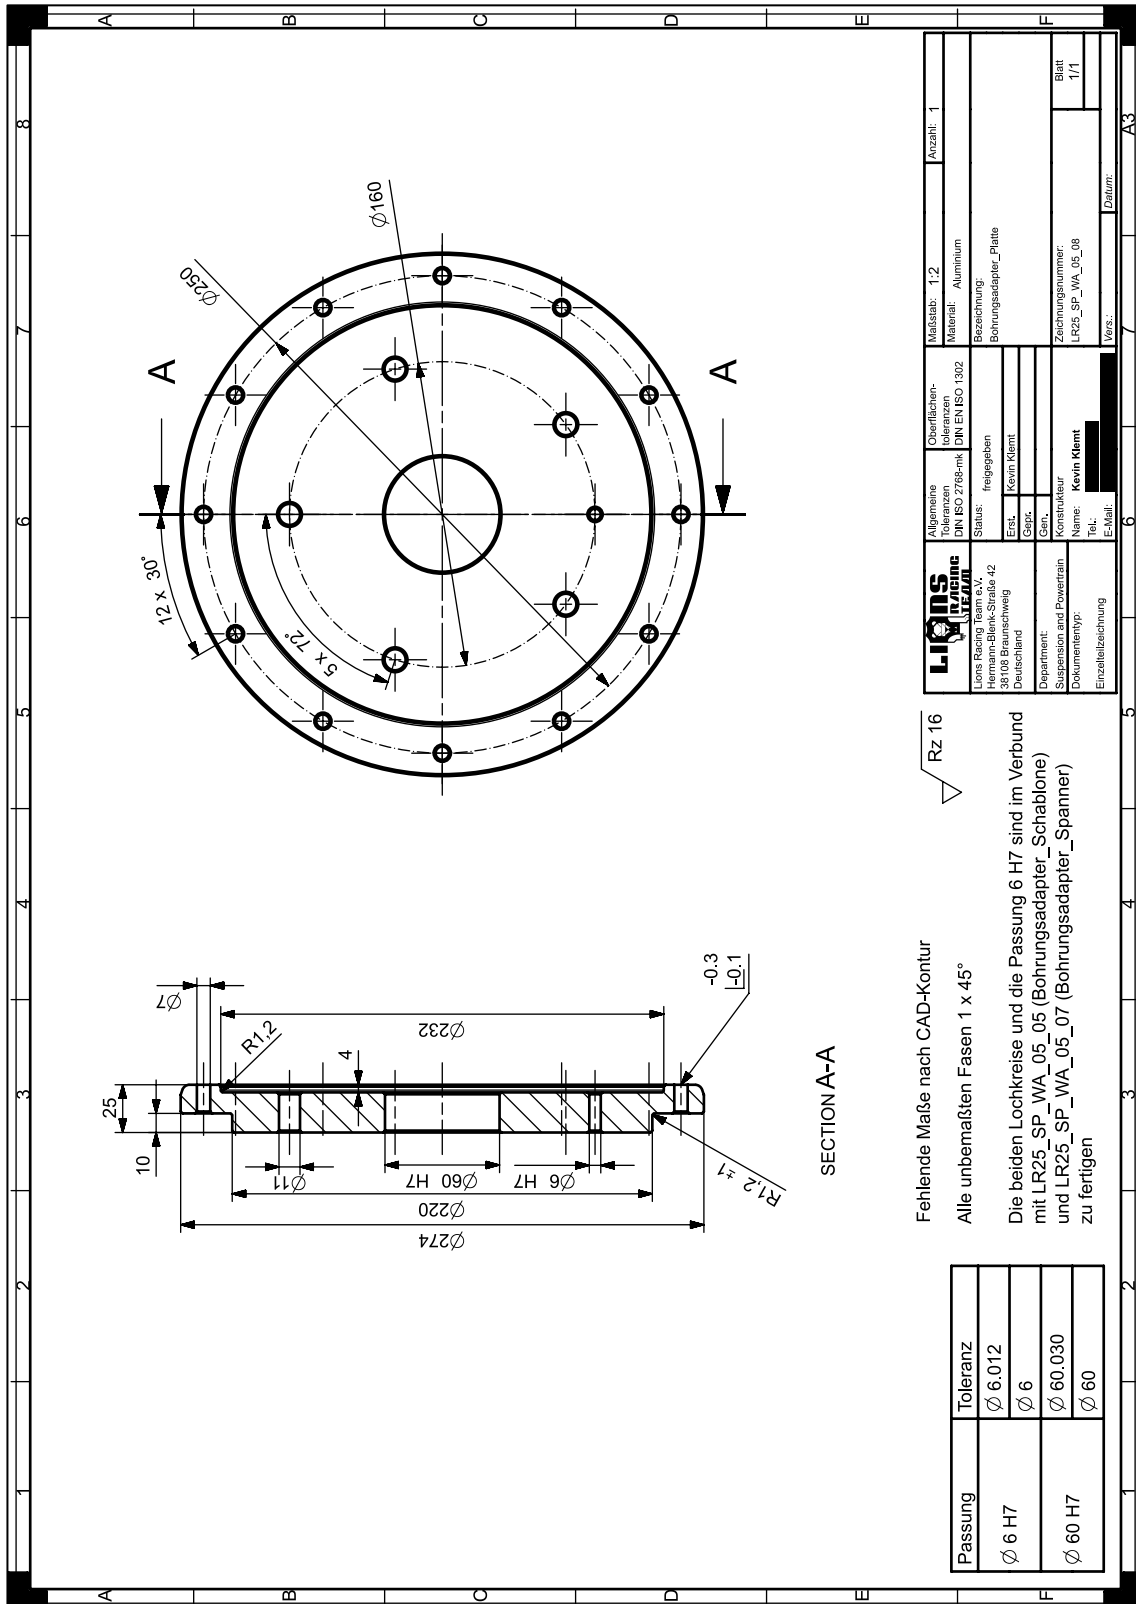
Technische Zeichnung Bohradapter (4/4); Platte [42]
